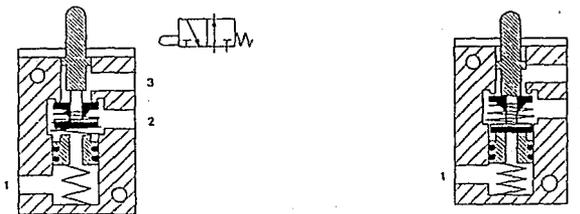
VALVULA 3/2 NA DE ASIEN TO PLANO.
